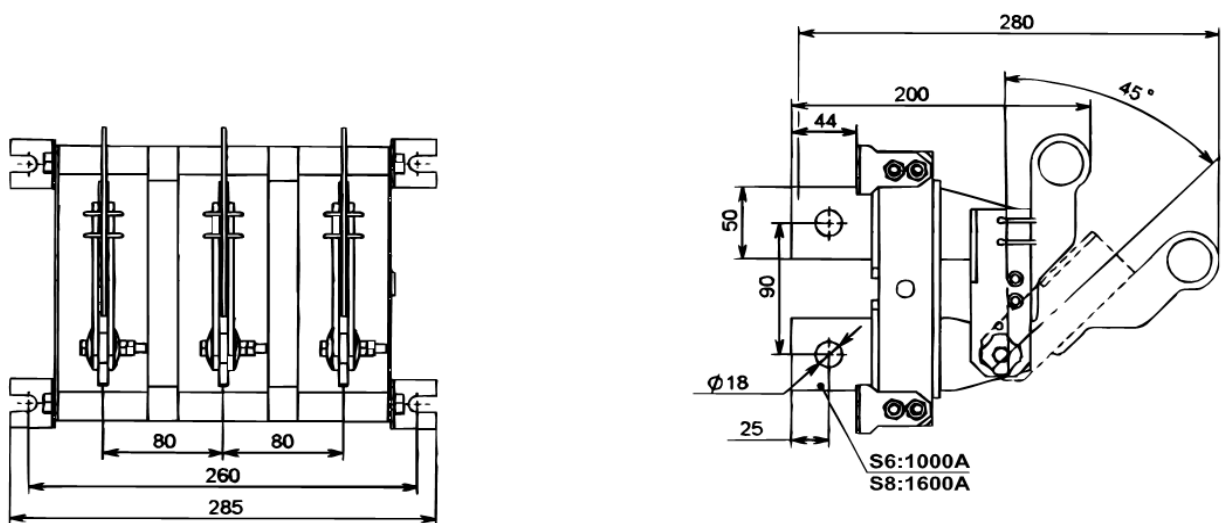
Разъединитель РЕ19 трехполюсный с рычагом для пополюсного оперирования штангой, заднего присоединения шин.
